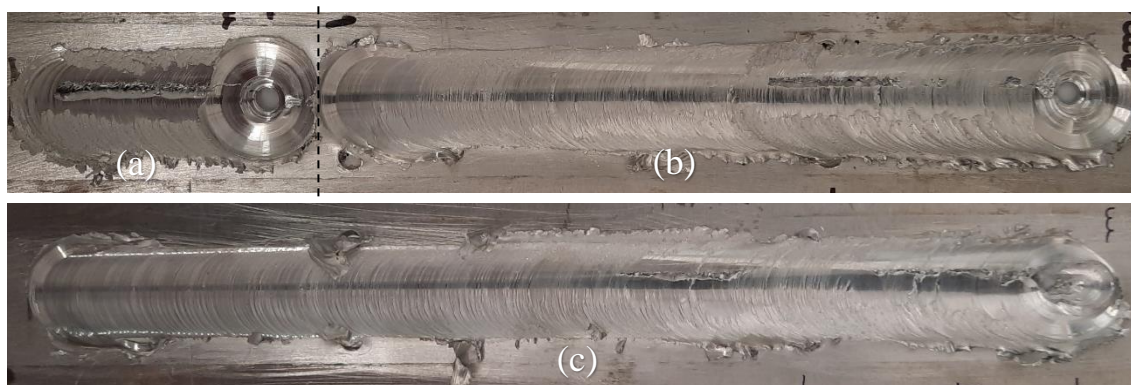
Aspetto superficial das soldaduras FSW Al-Mg: (a) D-870-60-6,9, (b) D-870-60-7 e (c) D-870-40-7.
